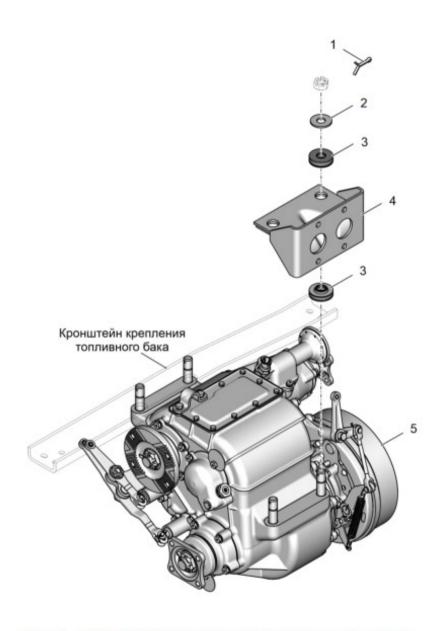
4320П-1800008-30 Установка раздаточной коробки
